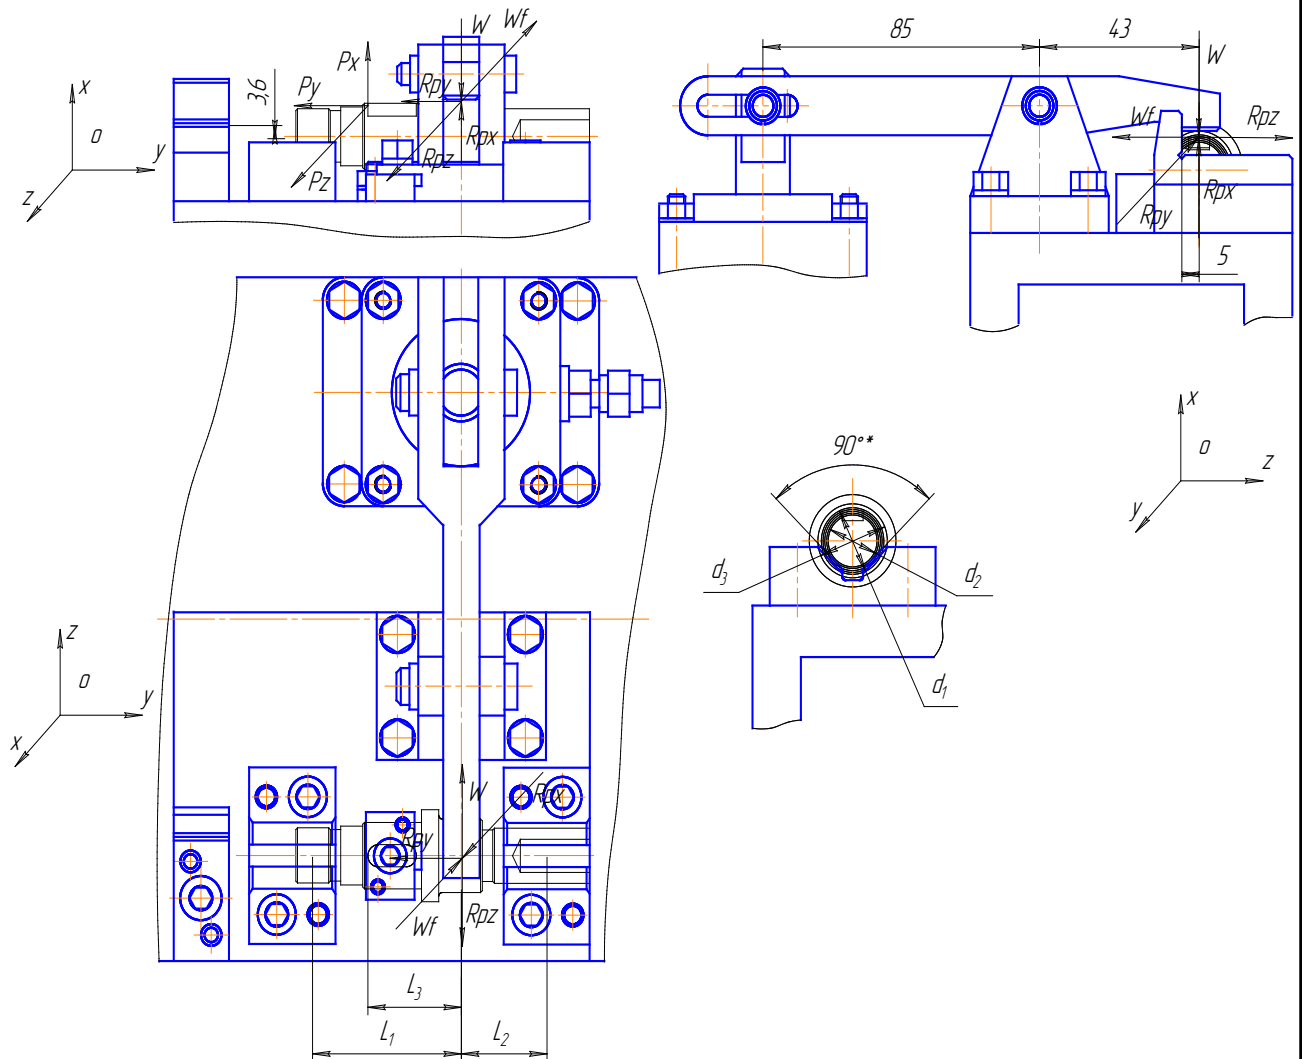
Розрахункова схема дії сил на деталь при фрезеруванні пазів $b=8P9$
